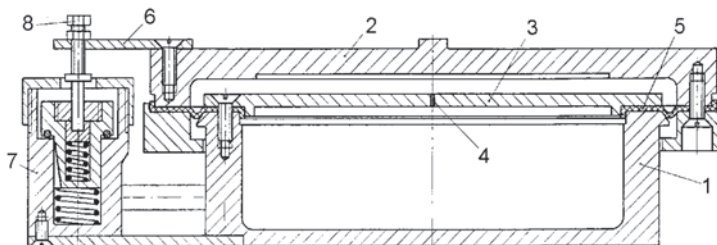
Конструктивная схема пневматической виброизолирующей системы:
